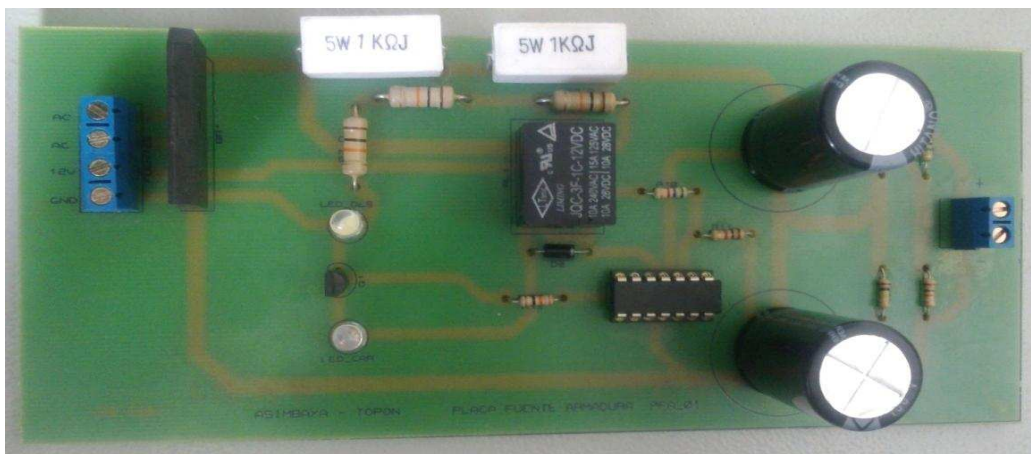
2 Tarjeta Ensamblada de la Fuente de Armadura
